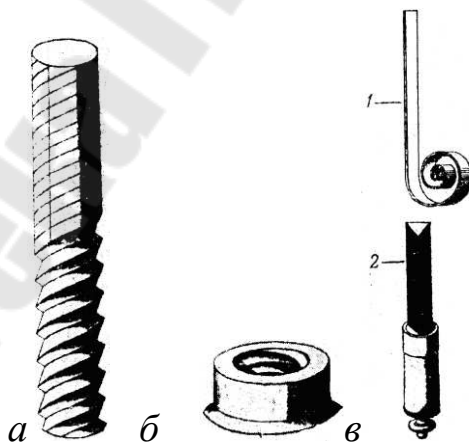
Эскизы винта (а), гайки (б) и инструментов для разметки и изготовления (в) (Жак Бессон, 1569г.): 1- лента, 2- напильник
